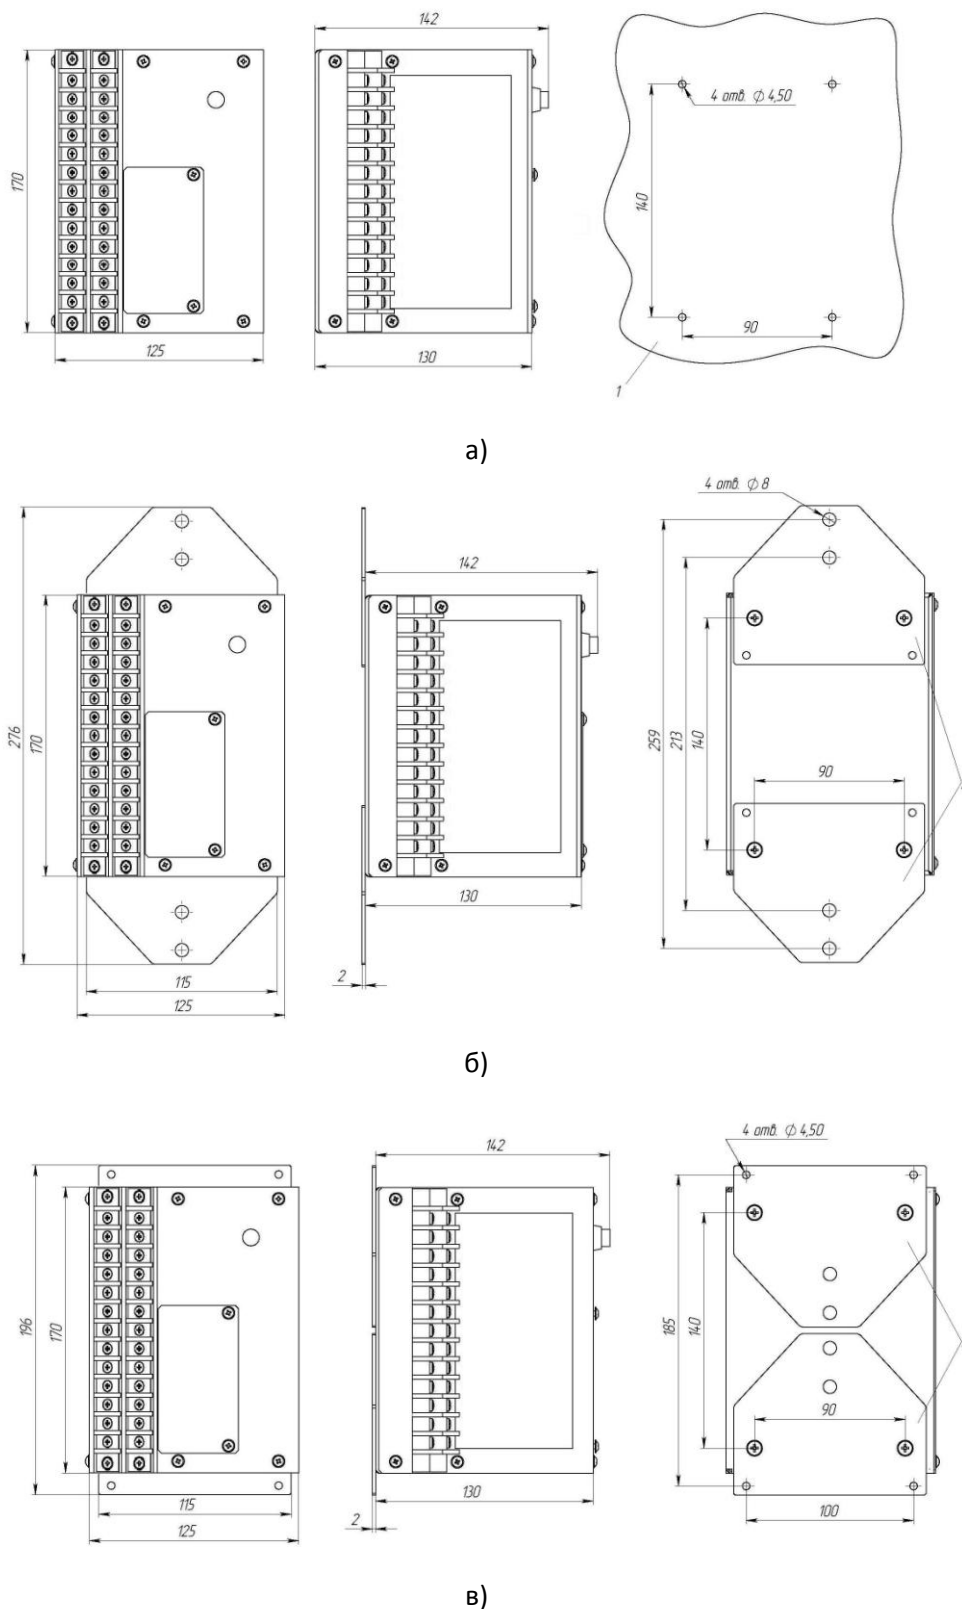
Габаритные и установочные размеры РЗМ-А:
